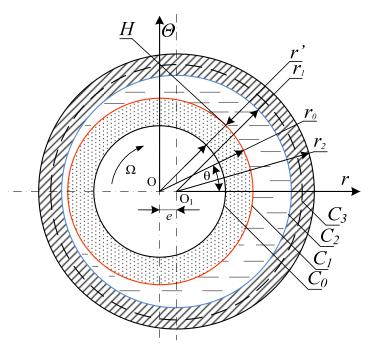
Схема радиального подшипника с пористым покрытием на поверхности шейки вала
